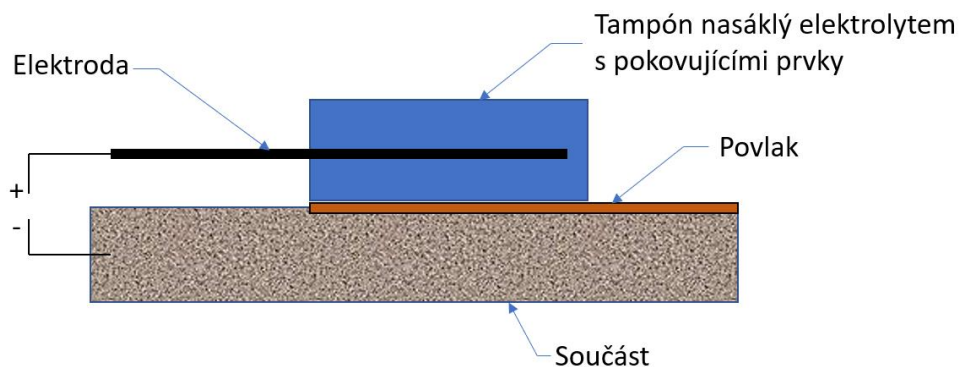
Schéma galvanického pokovování. Inspirováno dle [28]
